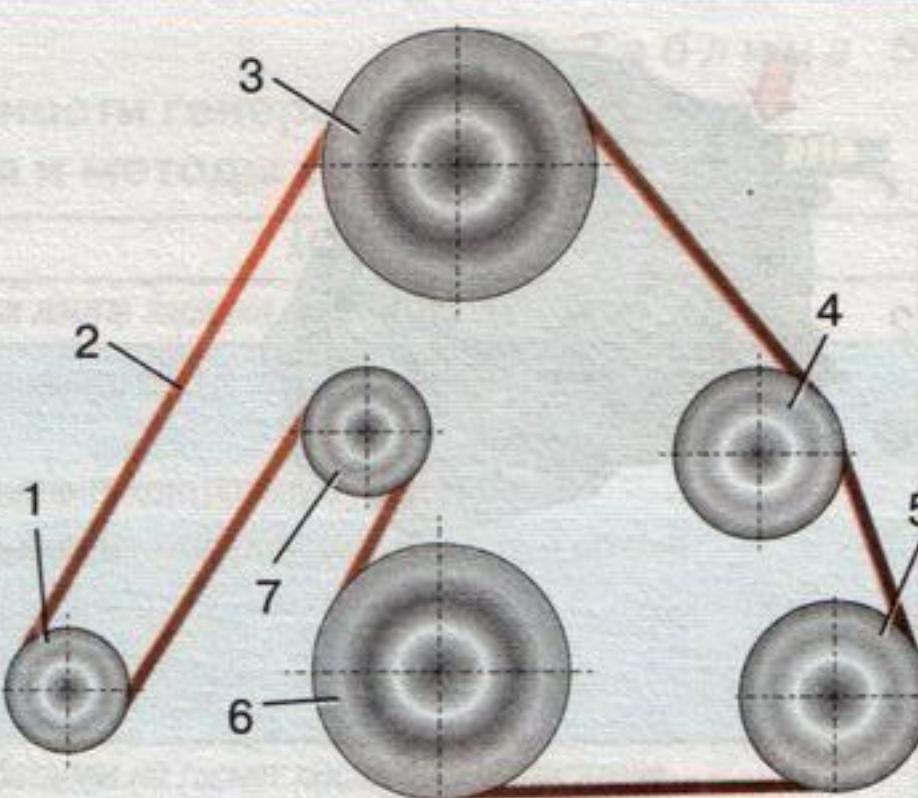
Схема установки ремня привода агрегатов бензинового двигателя рабочим объемом 2,8 л: 1 – шкив генератора; 2 – ремень привода агрегатов; 3 – шкив насоса гидроусилителя рулевого управления; 4 – шкив вентилятора охлаждения двигателя; 5 – шкив компрессора кондиционера; 6 – шкив коленчатого вала; 7 – натяжной ролик
